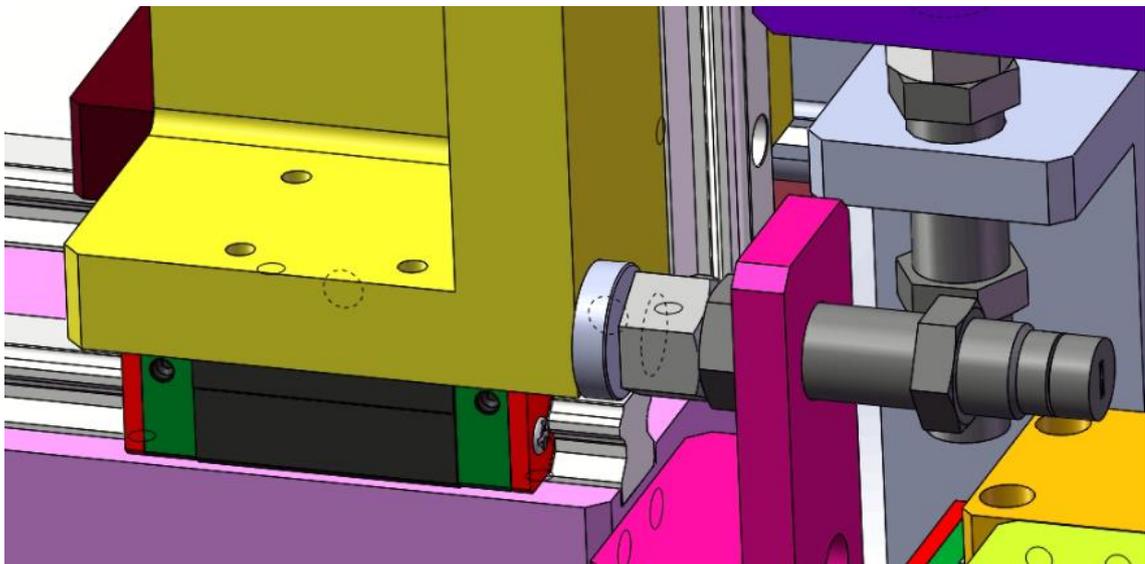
Amrtiguador y tope de recorrido. Fuente:propia
